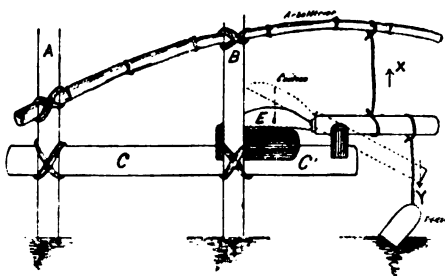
MACHINE A DÉFIBRER L'ABACA.
